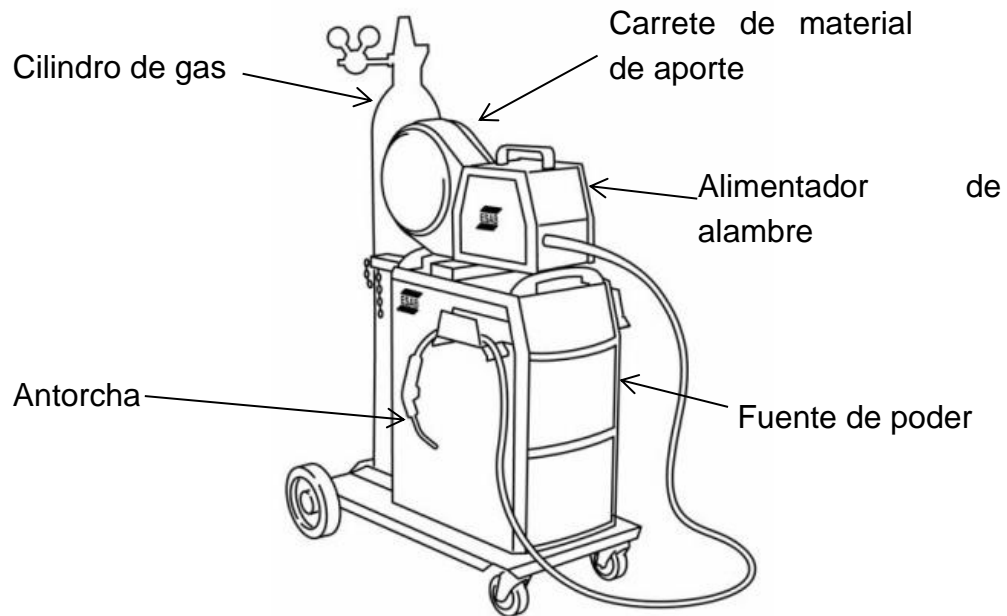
10 Equipo para soldadura MIG y MAG (16).
